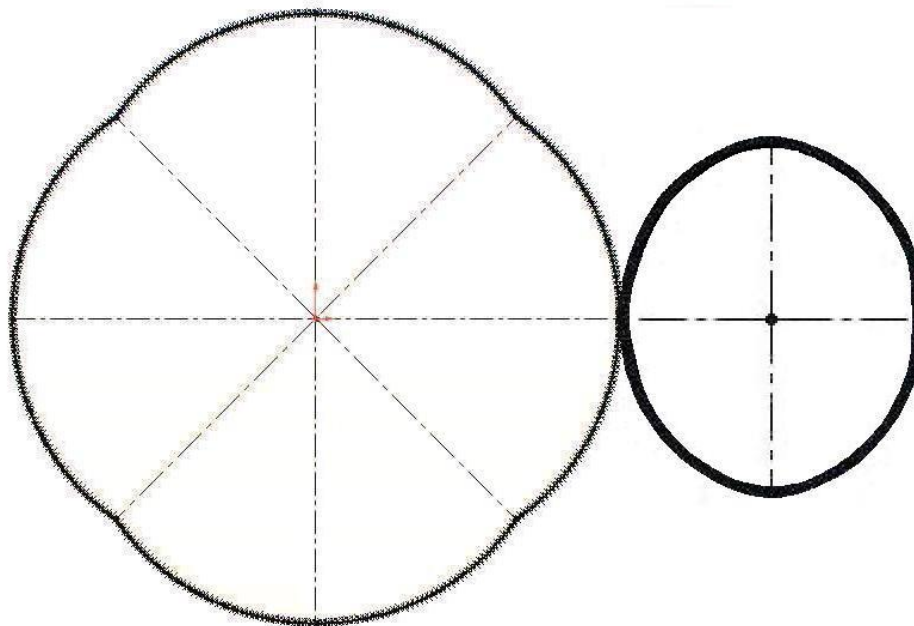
Начальные линии зубчатой передачи силового привода колесно-шагающего движителя
